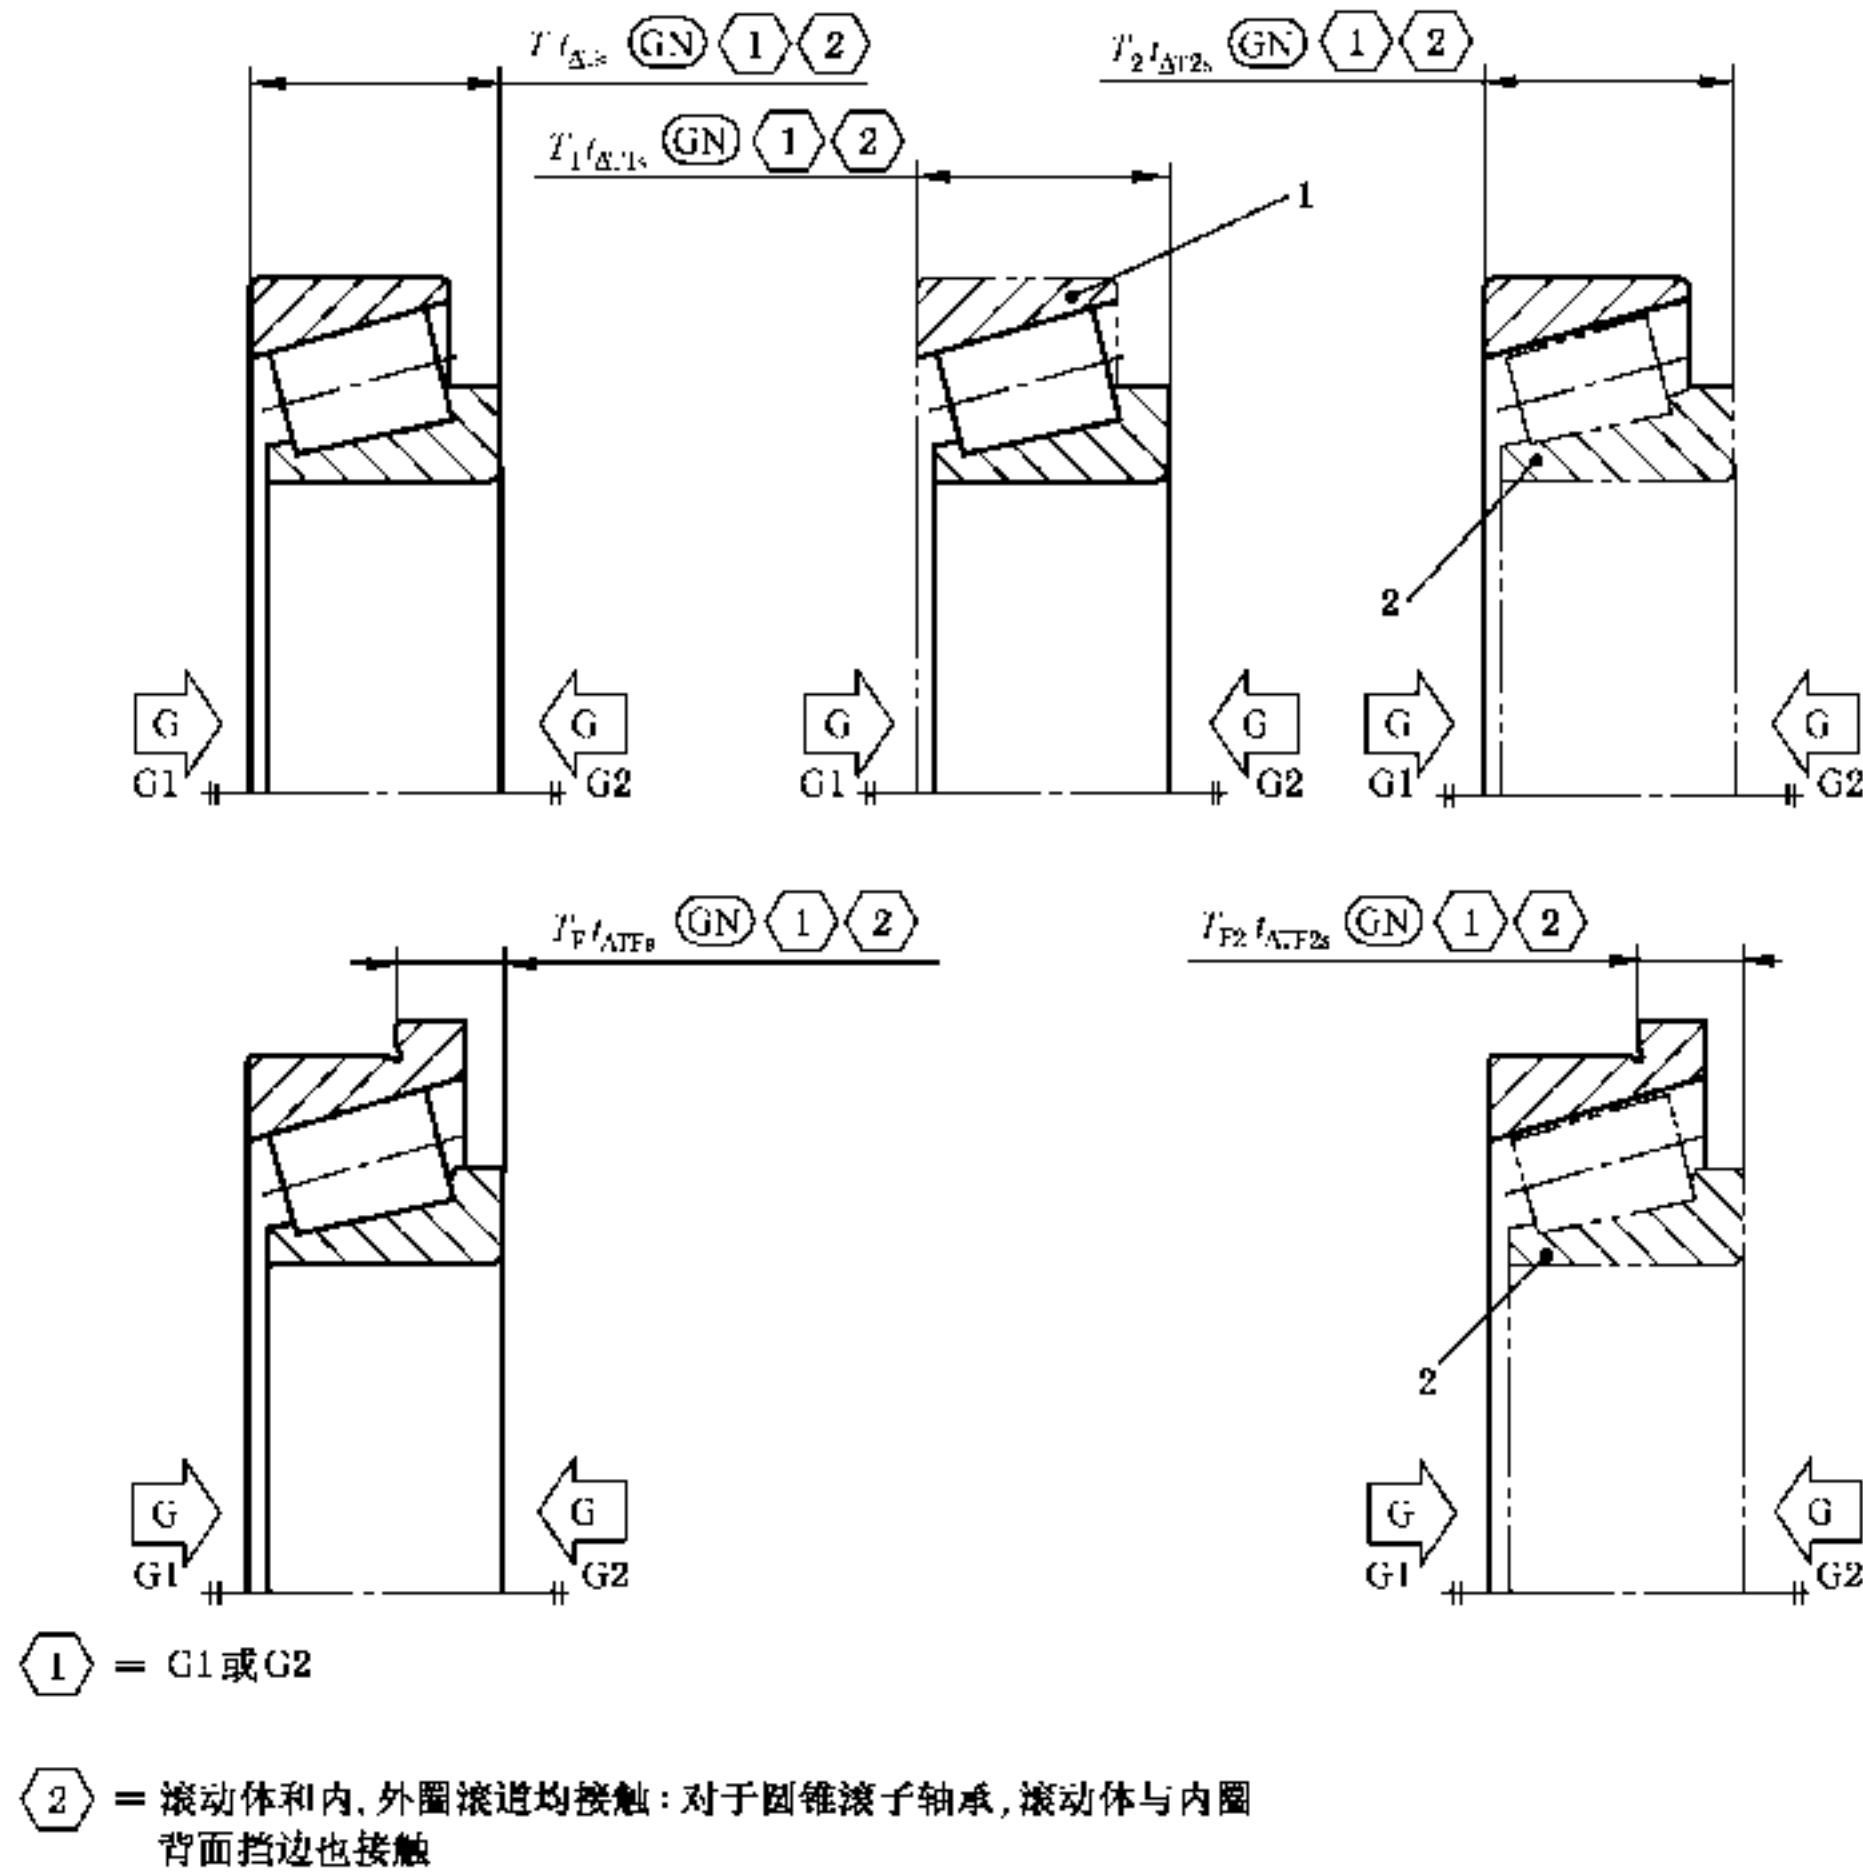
凸缘外圈成套轴承的几何公差——单列角接触球轴承和圆锥滚子轴承
